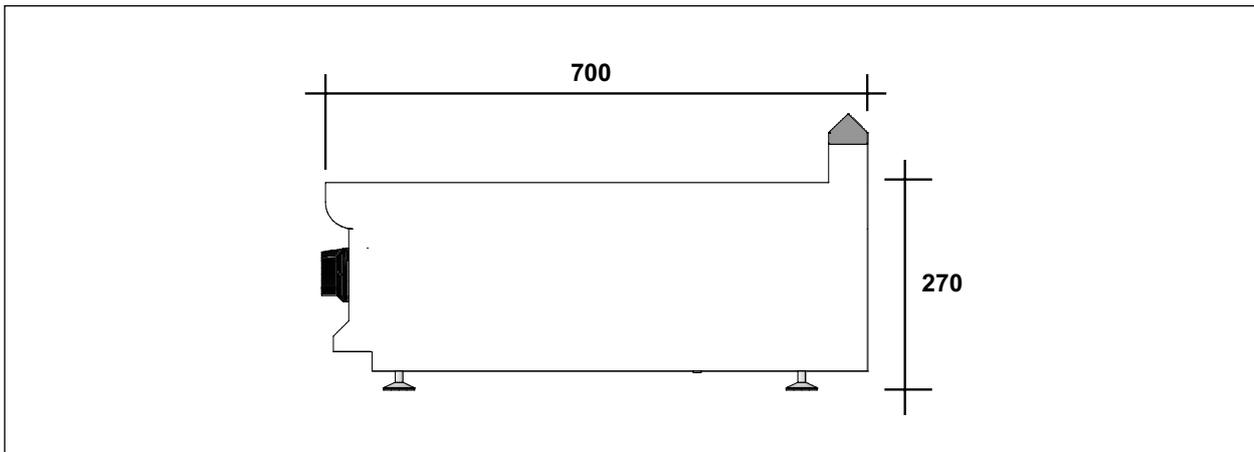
Dimensions de la cuisinière de comptoir en vitrocéramique
